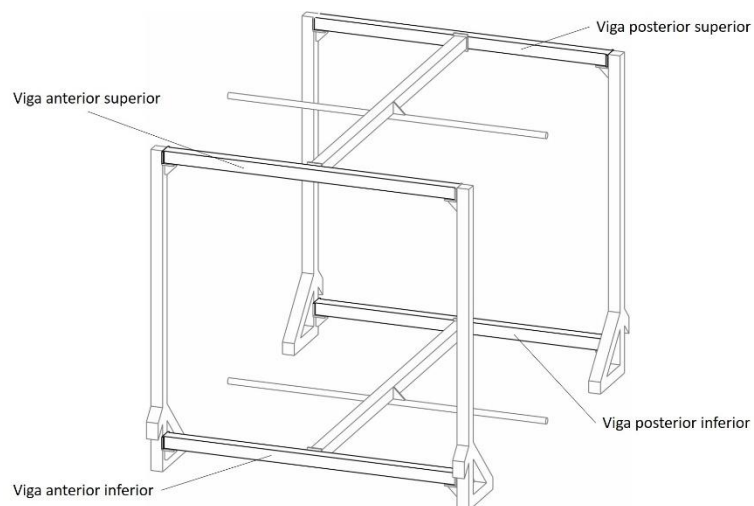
Elementos fijos del Banco KLT. La estructura del banco KLT está formada por cuatro columnas, cuatro vigas transversales y dos vigas longitudinales.
